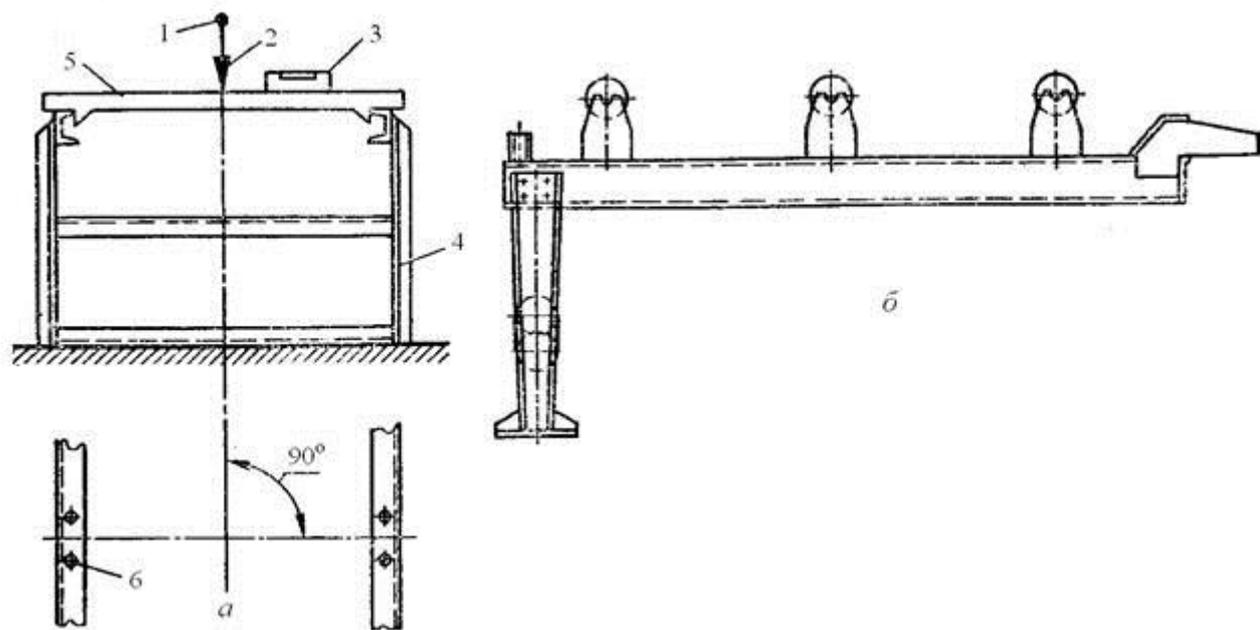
Схема подготовки металлоконструкции к монтажу:
